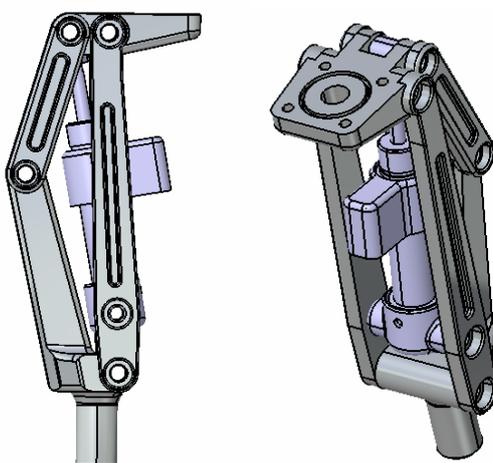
Diseño final construido de Prótesis de rodilla policéntrica
